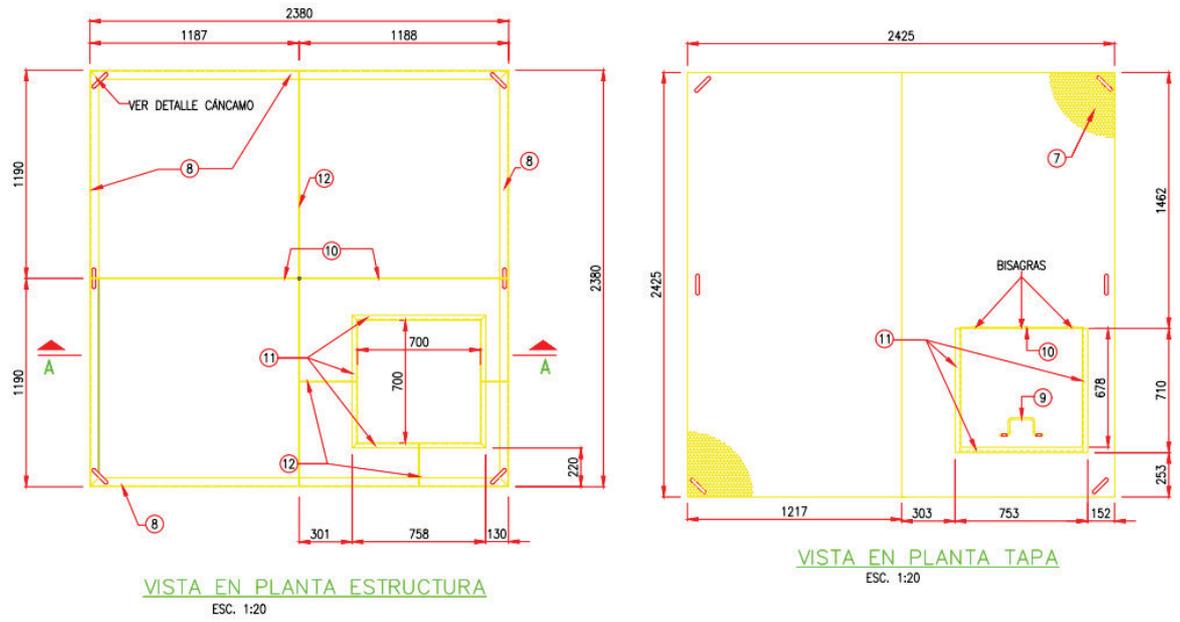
Vista en planta de tapa metálica. Estructura metálica y exterior.
